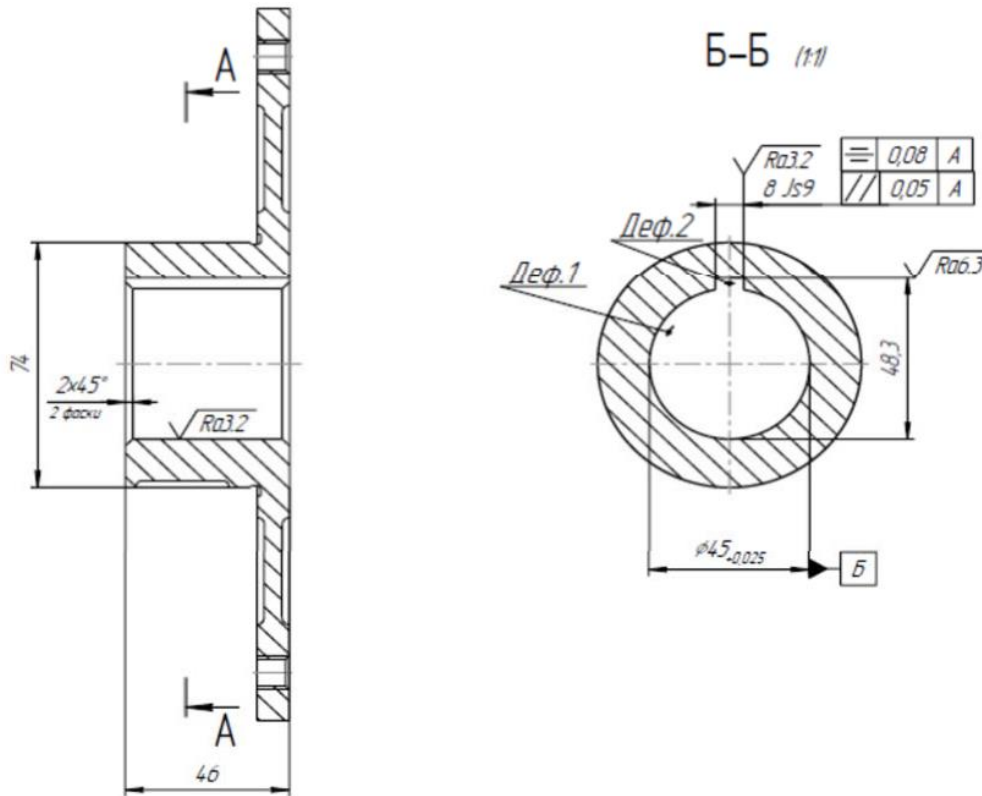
Ескіз ремонтного кресленика деталі
